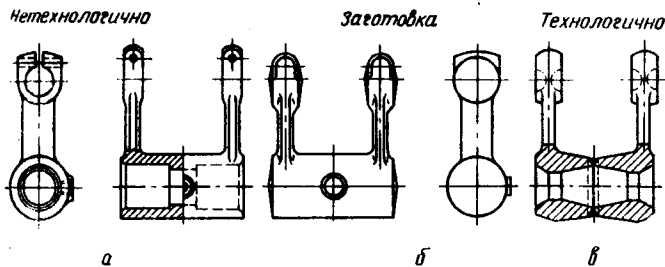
Качалка с тонкими длинными рычагами (а) из штампованной заготовки (б) и качалка, сваренная из штампованных элементов (в).
